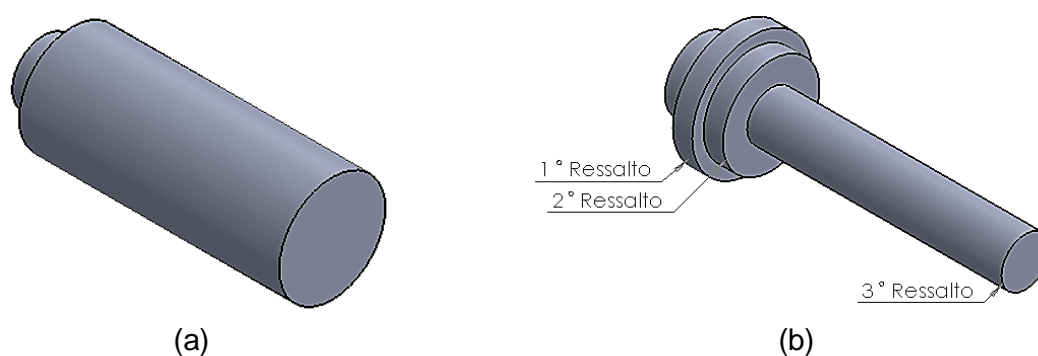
Formato dos corpos de prova: (a) antes da usinagem; (b) após a usinagem.
